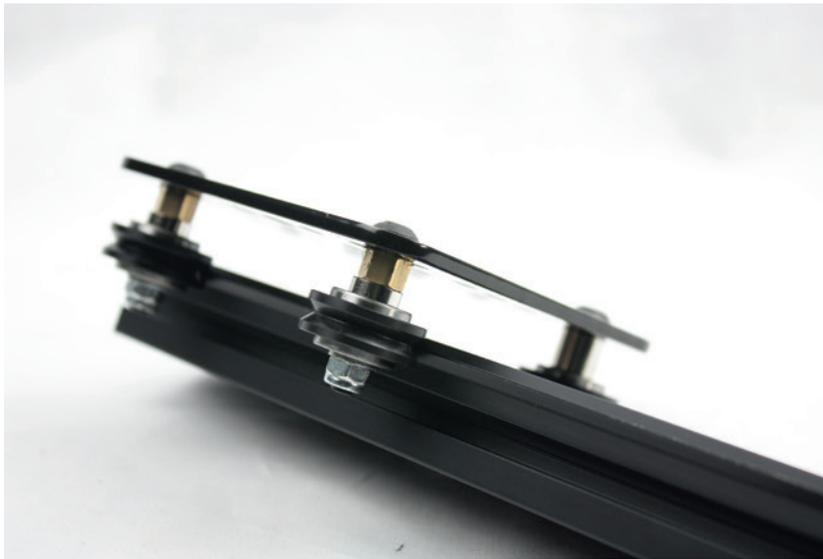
Die Achsen der Fräse sind hier mit Linearführungen in Form von V-Rollen realisiert.
